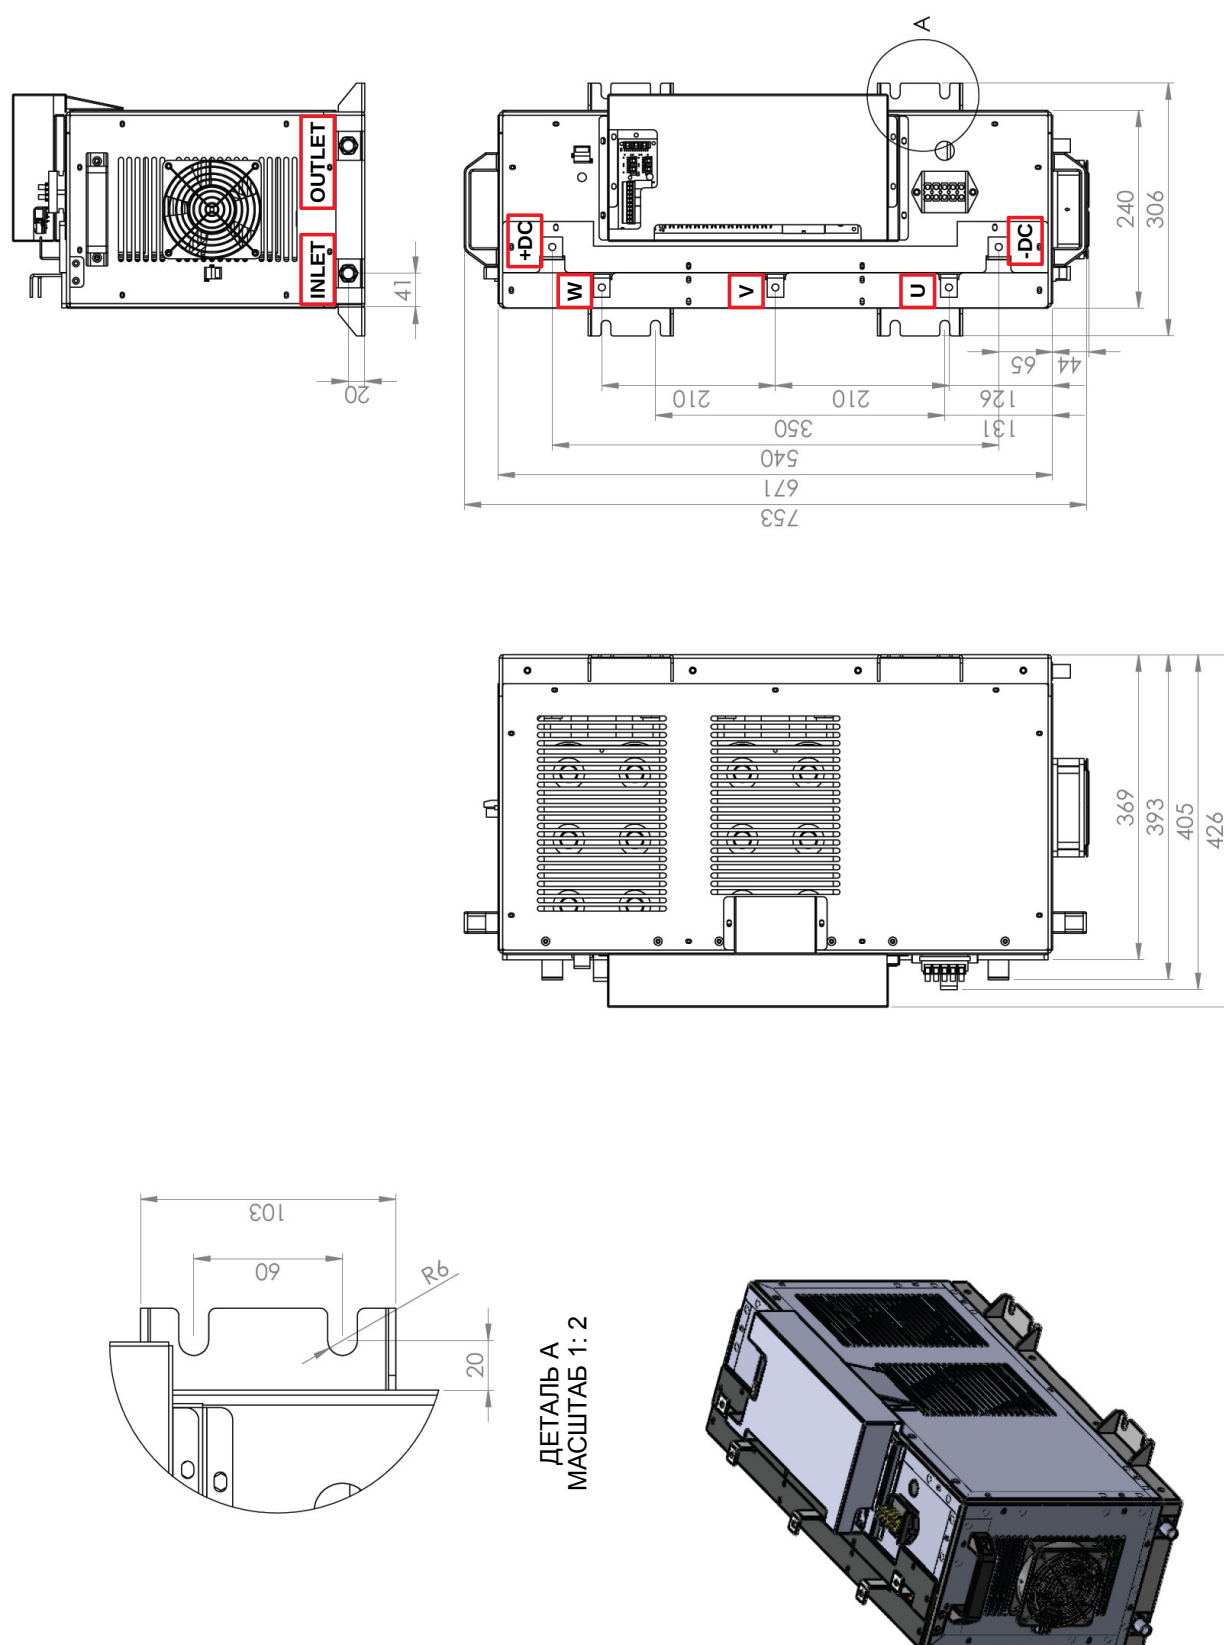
Модуль 1/3 - блок мощности с платой PCB MFC810/05
